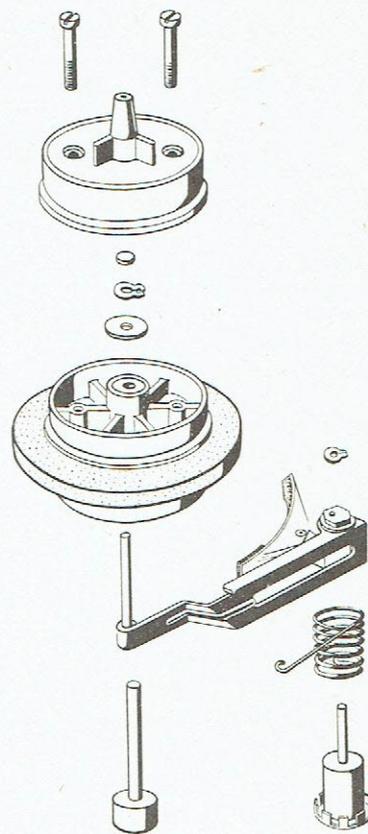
Vue éclatée des plateaux d'entraînement et des freins
